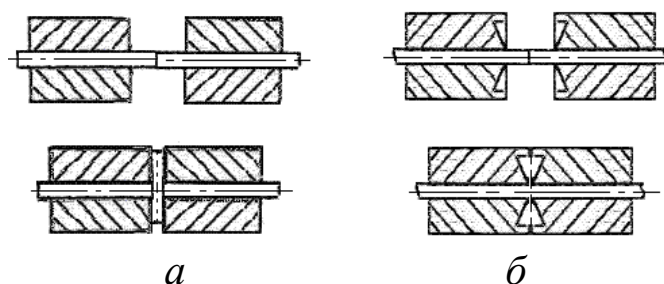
Схемы сварки в зажимных губках: *а* – с плоскими торцами; *б* – с заостренными торцами (вверху – до сварки, внизу – после сварки)
